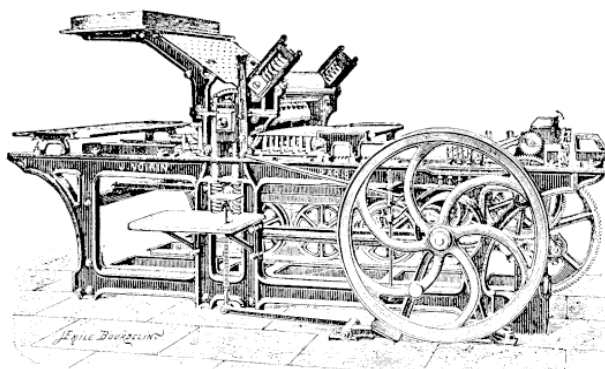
Machine à deux cylindres pour l'impression de la tôle et du fer-blanc par report de caoutchouc.
